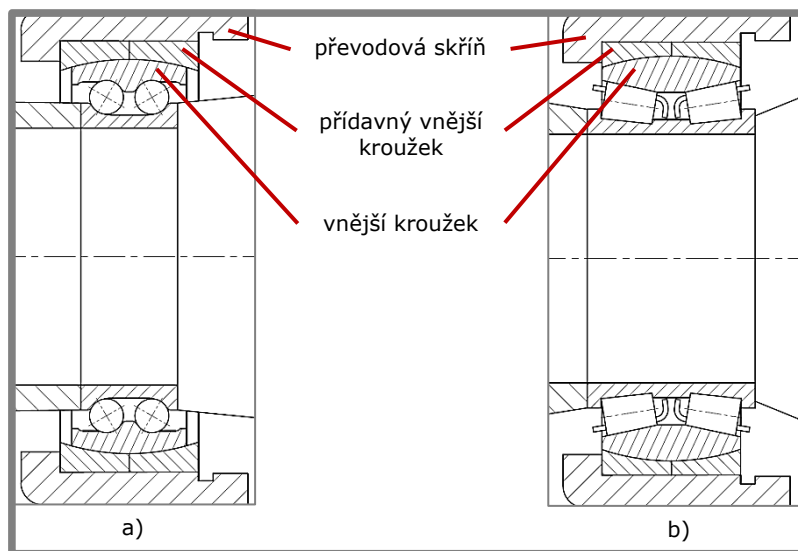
Soudečkové ložisko a) standardní, b) s rozšířeným vnějším kroužkem [13]
